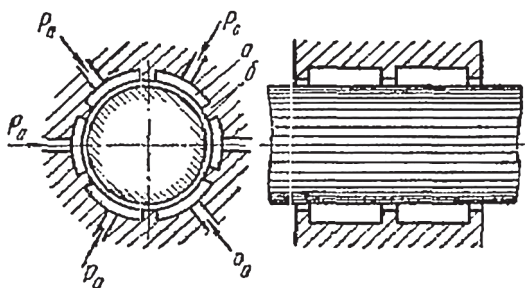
Схема подшипника с воздушной смазкой под давлением:
